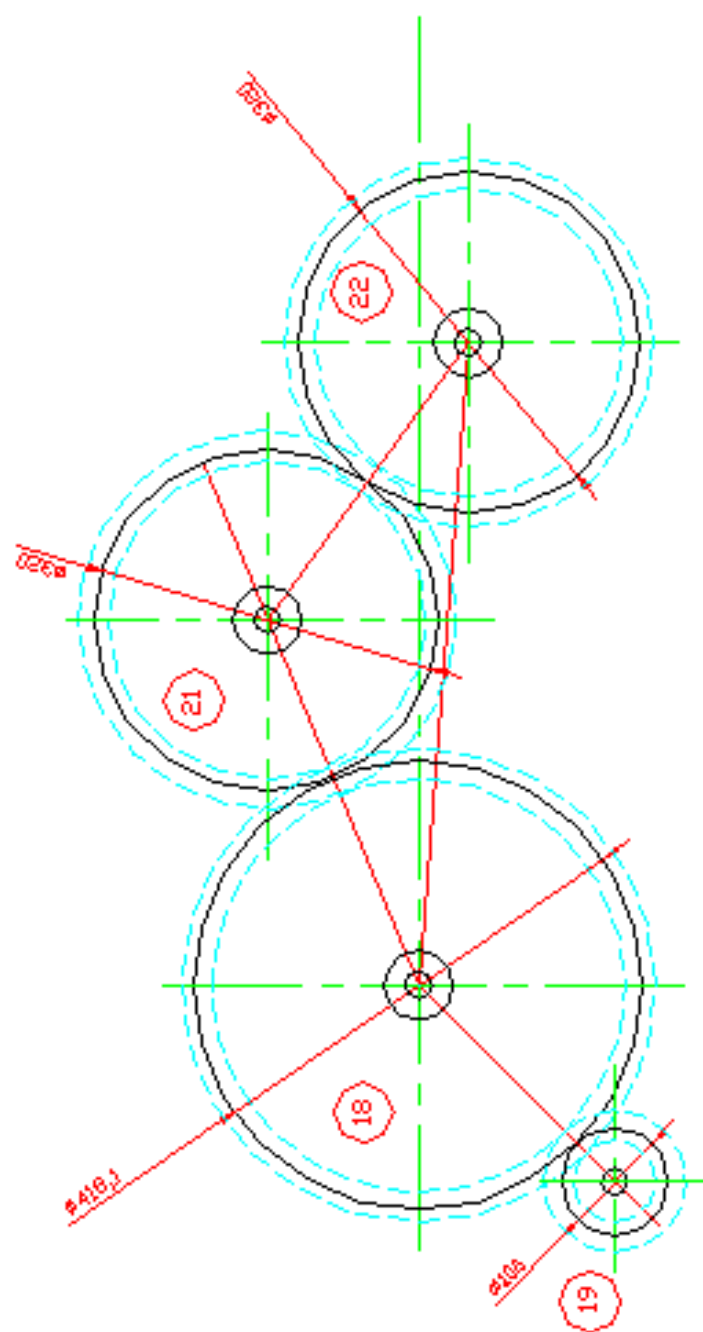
TREN DE ENGRANAJES Y SUS DIMENSIONES
